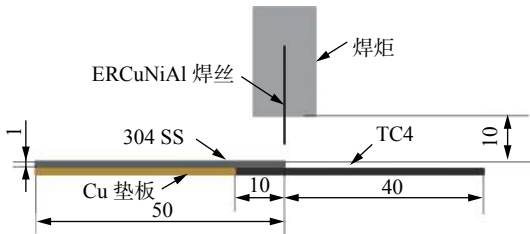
CMT 焊接 TC4/304 SS 示意图 (mm)
